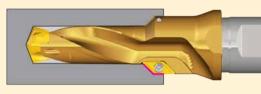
Схема сверления и дополнительного растачивания за один проход ступенчатого отверстия сверлом DRILLRUSH с боковыми пластинами.
